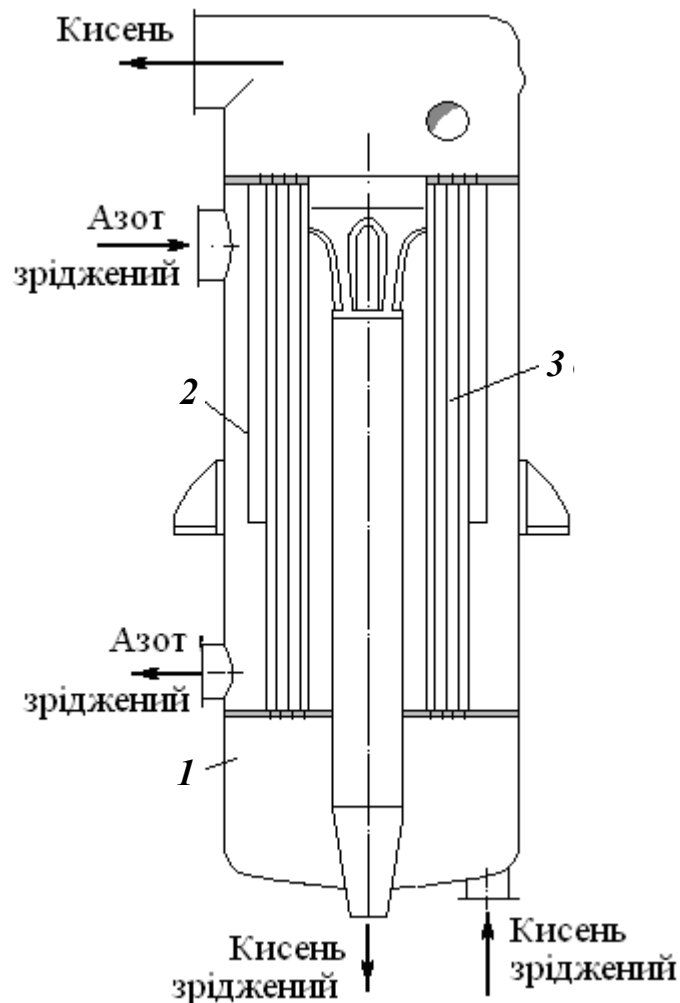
Основний конденсатор-випарник: 1 — корпус; 2 — обичайка; 3 — трубки
